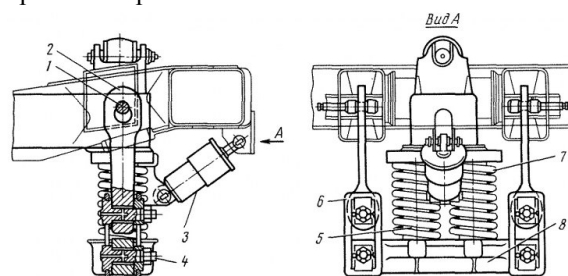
Центральне ресорне підвішування метровагонів Е, Еж, їх модифікацій і 81-717, 81-714: 1- валики центрального підвішування; 2 - серга; 3-гідравлічний амортизатор; 4- валик; 5- внутрішня пружина; 6 - підвіска рамочна; 7- зовнішня пружина; 8 - піддон.
